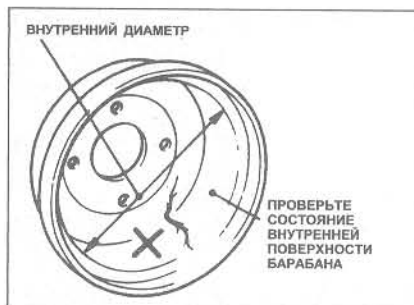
Проверка тормозных барабанов (Глава 21)
